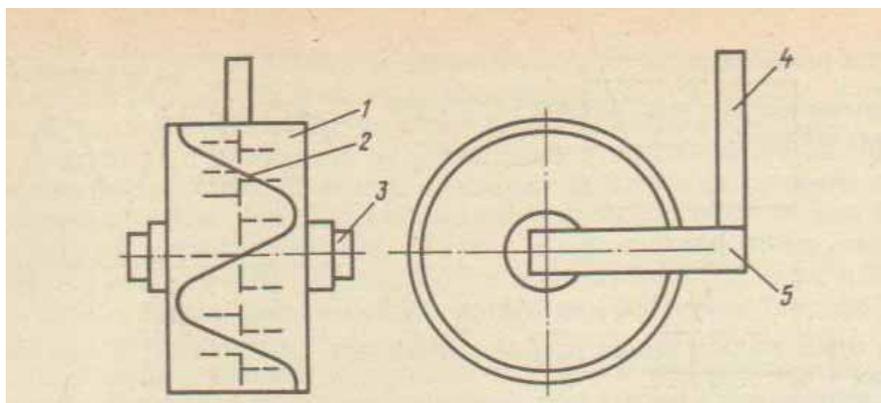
Каток – бороздодел КБ-1 : 1- цилиндр; 2 – выступ; 3 – ось; 4-стойка; 5 – вилка.
